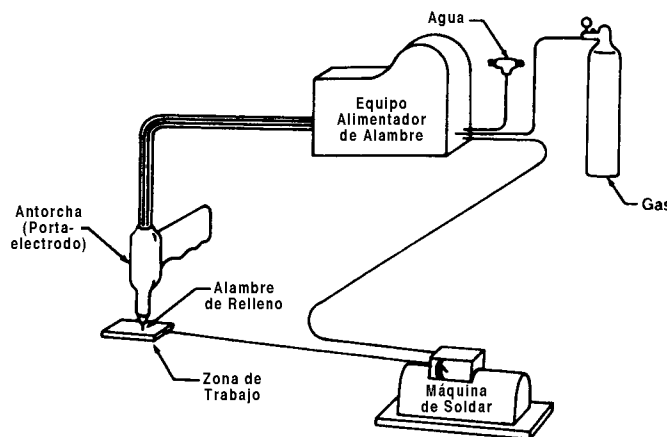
Soldadura por Arco Metálico en Atmósfera Inerte (MIG)
